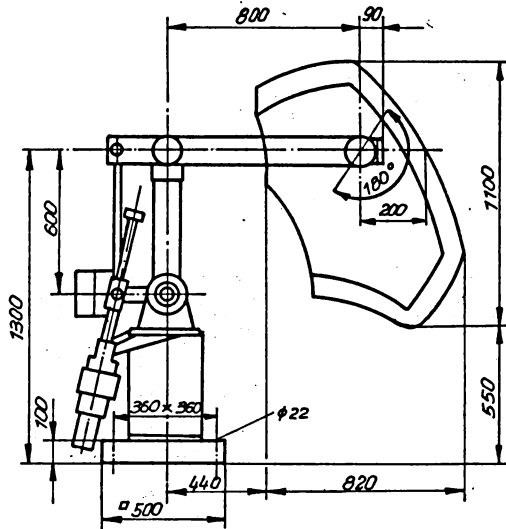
Hauptabmessungen und Bewegungsbereich des IR
